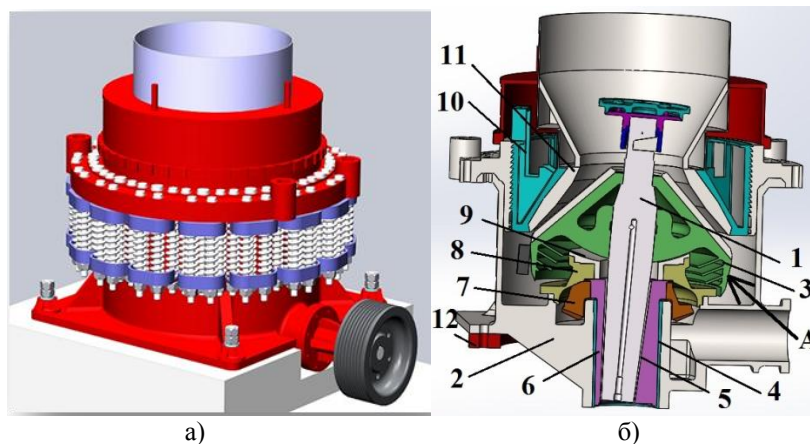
Твердотіла 3D модель конусної дробарки КМД-1750 (а) та її адаптована модель для динамічного дослідження в модулі Motion (б): 1 – конус рухомий; 2 – корпус дробарки; 3 – корпус рухомого конуса; 4 – втулка проміжна; 5 – втулка конічна; 6 – ексцентрик; 7 – конічна шестерня приводу конуса; 8 – опорна чаша; 9 – під'ятник; 10 – конус нерухомий; 11 – броня нерухомого конуса; 12 – фланець для збору динамічних навантажень.
